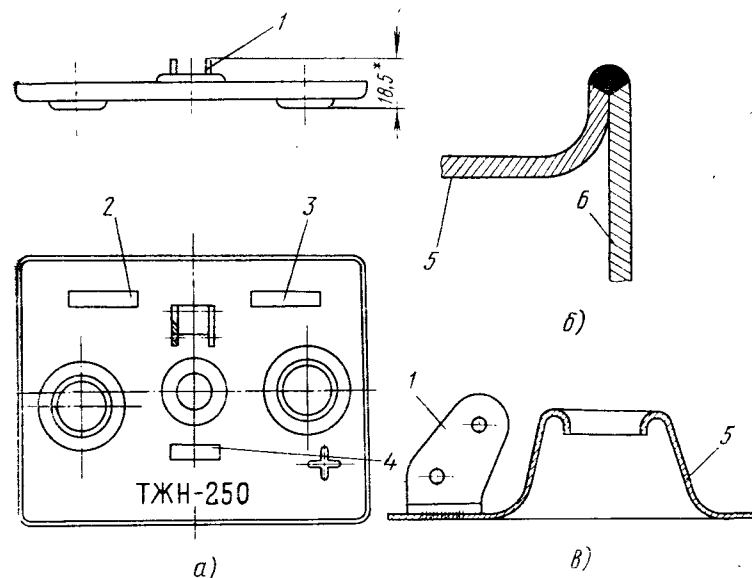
Крышка аккумулятора ТЖН-250 (*a*), узел приварки крышки к корпусу (*б*) и кронштейн для клапанной пробки (*в*):
